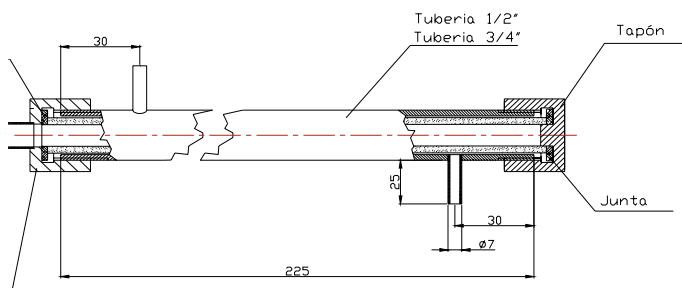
Esquema del diseño mecánico del *housing* para membranas tubulares.
